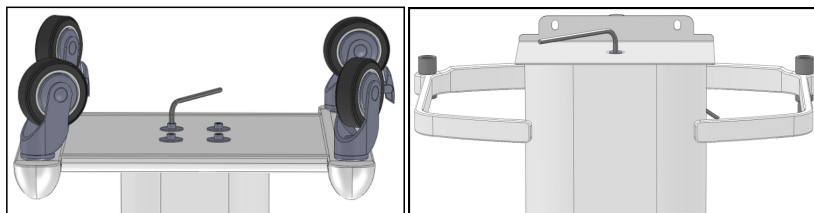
Ступени сборки мобильной стойки. Слева – установка вертикальной опоры. Справа – установка подноса.
